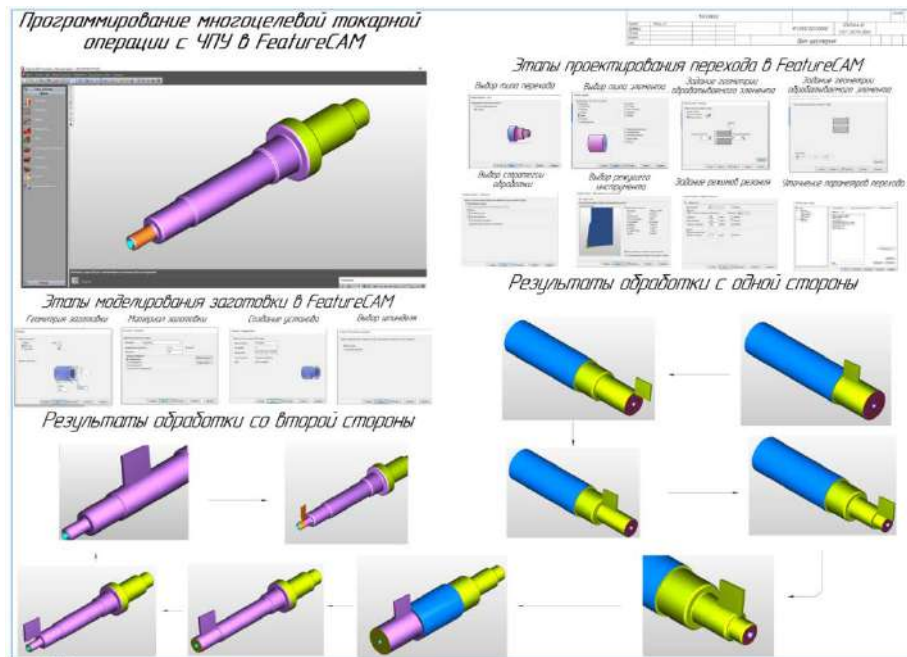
Обработка ДСЕ вал-шестерни на станке с ЧПУ.
